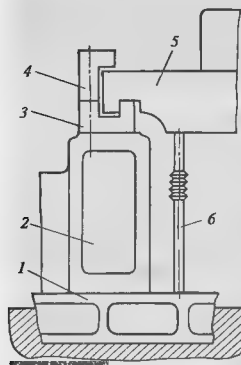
Установка дополнительной опоры под лапу для уменьшения силы, действующей со стороны лапы на корпус подшипника
